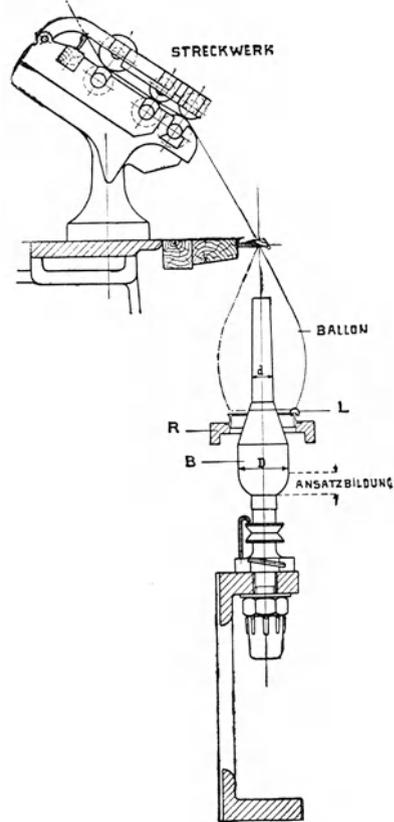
Wirkungsweise der Ringspinnmaschine.
